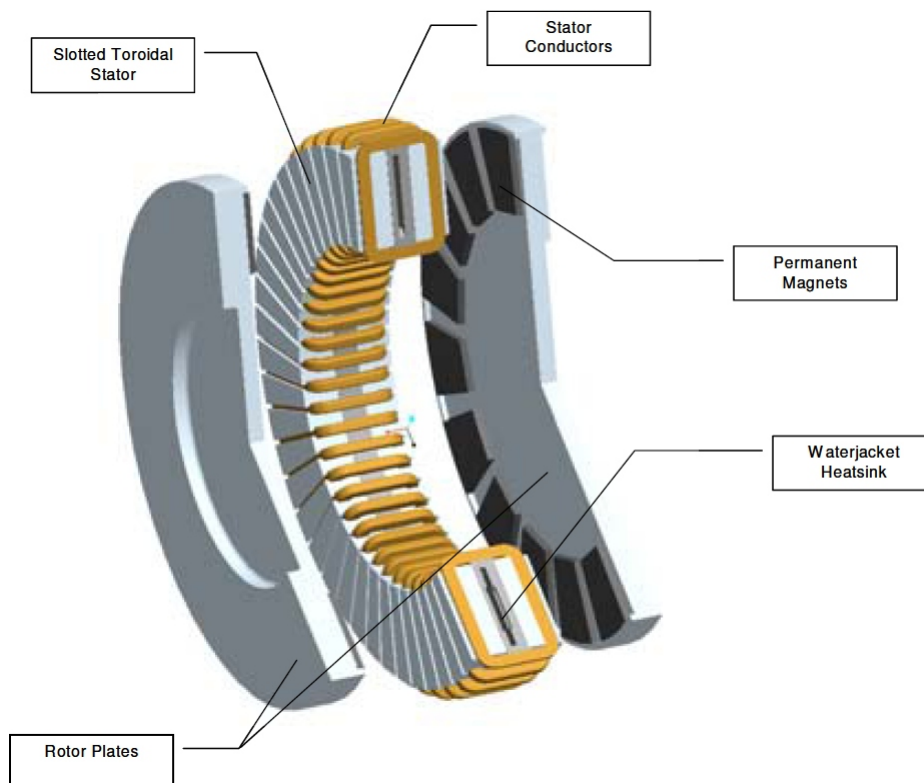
STATOR S VODNÍM CHLAZENÍM. PŘEVZATO Z [23].
